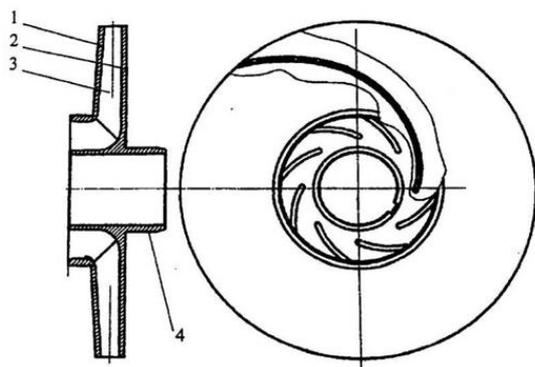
Закрытое рабочее колесо с плоской наружной поверхностью переднего диска:
